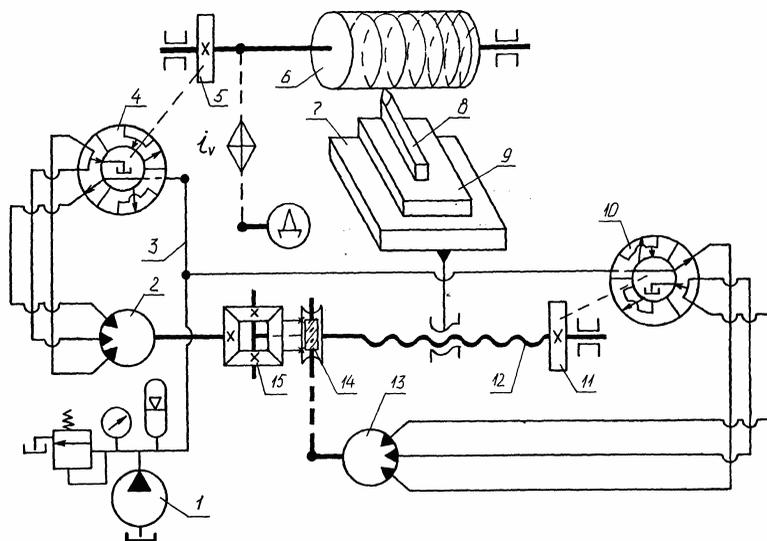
Схема резьбонарезного станка с гидравлическими связями для нарезания винтовых поверхностей переменного шага
